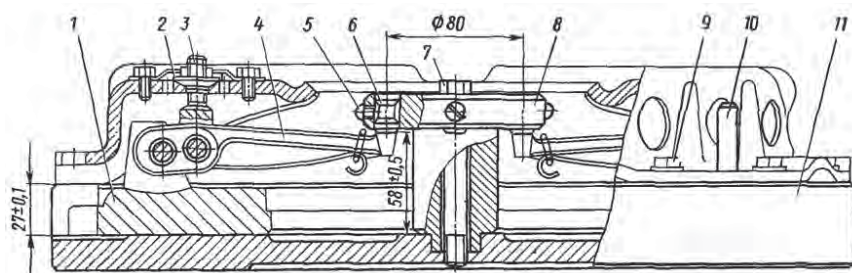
Приспособление для сборки и разборки нажимного диска с кожухом в сборе:
